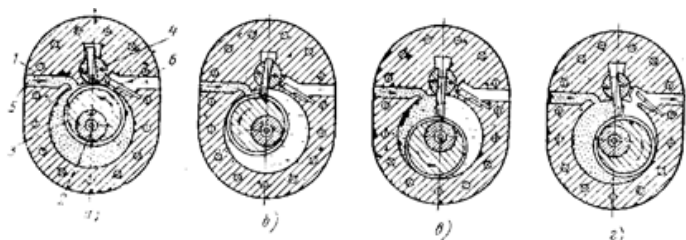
Схемы компрессора с катящимся ротором и качающейся разделяющей пластиной, прижимаемой к ротору:
